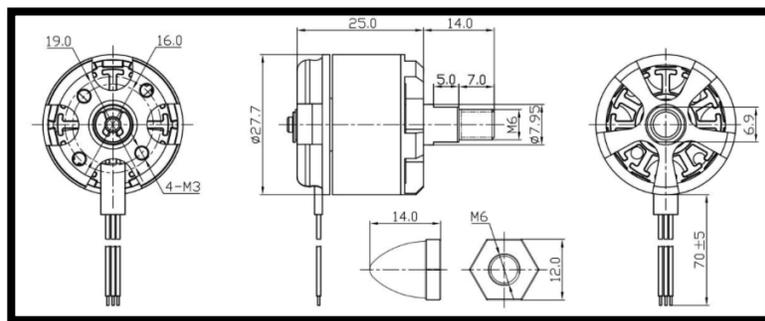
Dimensiones Motor rocket 2212 1000 KV.
